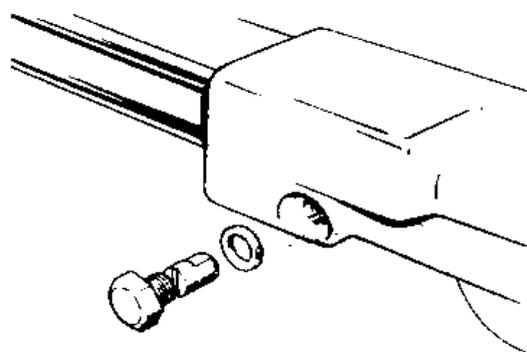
Выньте контрольные штифты корпусов подшипников (Разд.35)
